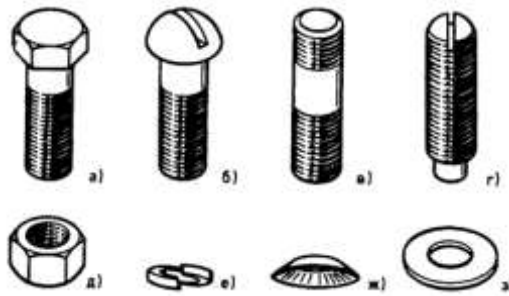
а — болт; б — винт; в - шпилька; г — установочный винт; д — гайка; е — пружинная шайба; ж — деформируемая шайба; з — плоская шайба
